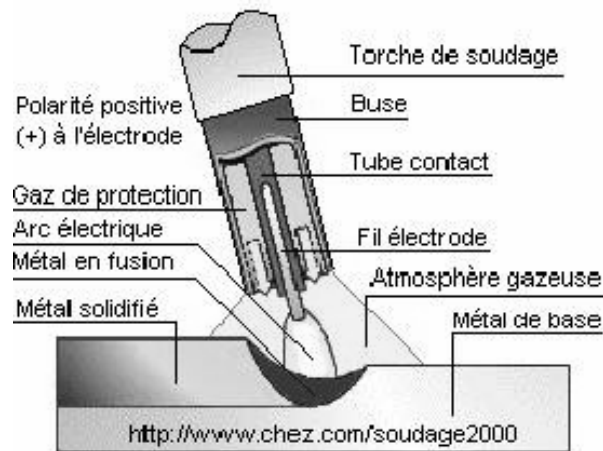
Procédé de soudage en M.I.G / MAG
